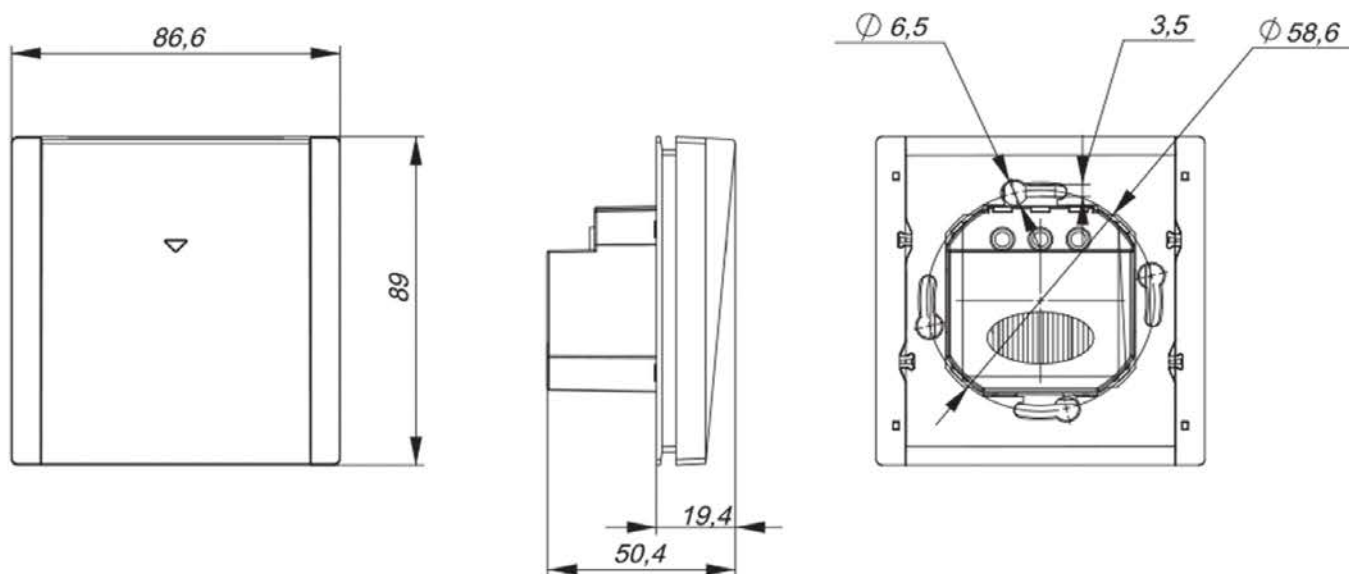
Габаритные и установочные размеры выключателя / Figure 2 – Overall and installation dimensions of the switch / 2 сурет – Ажыратқыштың габариттік және орнату өлшемдері / Figura 2 – Dimensiunile generale și de instalare ale întrerupătorului / 2-rasm – Viklyuchatelning gabaritlari bo'yicha va o'rnatilish natijasidagi o'lchamlari
